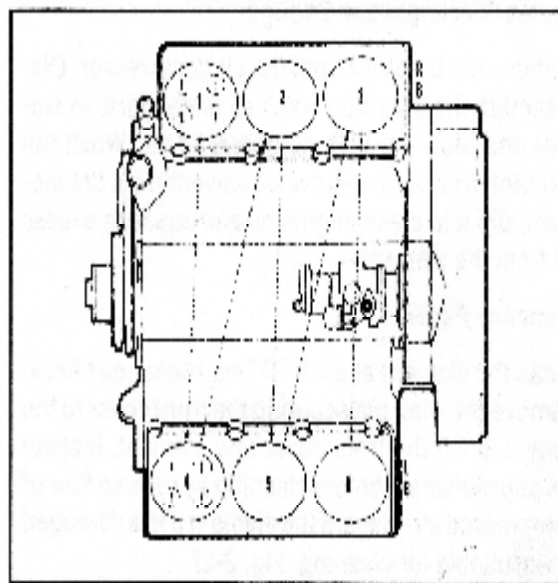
Порядок зажигания, двигатель V11461 V6
